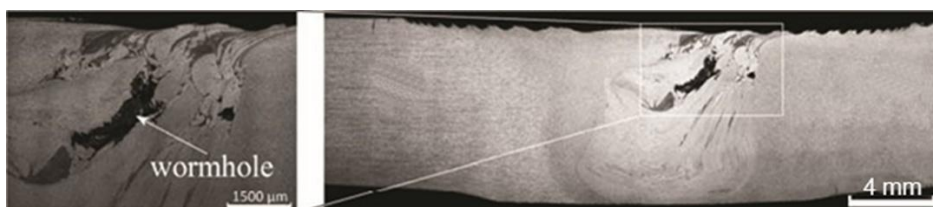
Defeito detectado no *Friction Stir Welding*, wormhole adaptado de [15]
